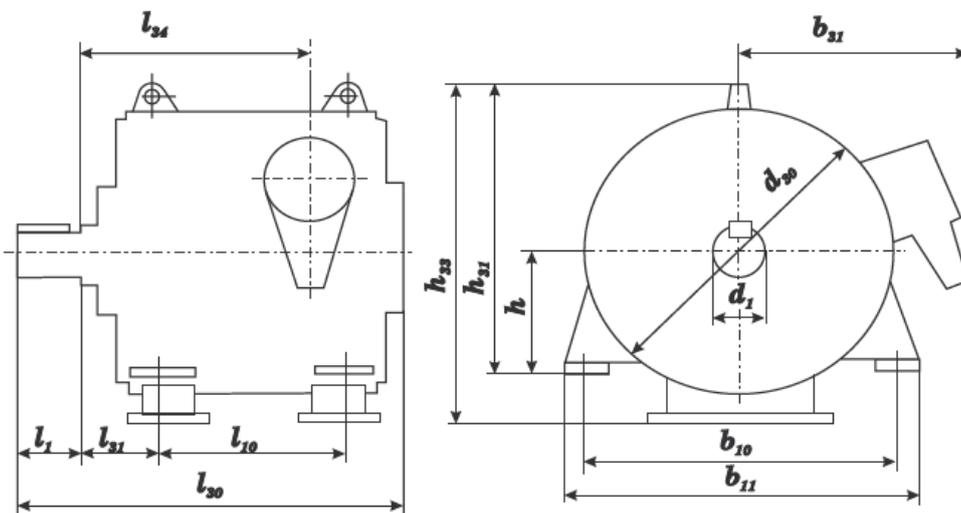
Габаритные, установочные, присоединительные размеры двигателей АНЗ-2
